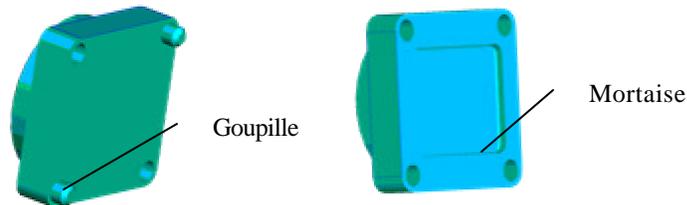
Alternatives de conception pour favoriser l'assemblage de la chape
